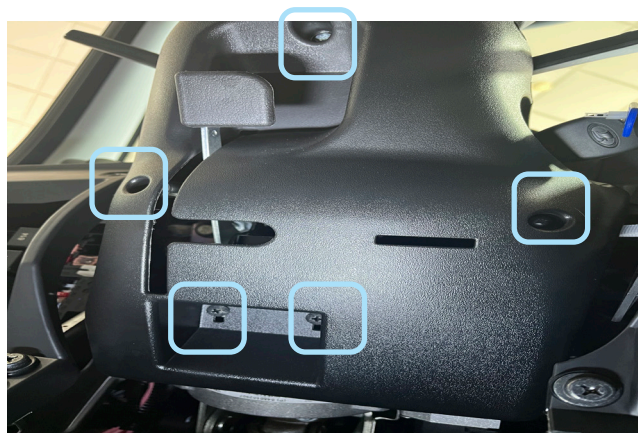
Саморезы крепления кожуха рулевого вала.
